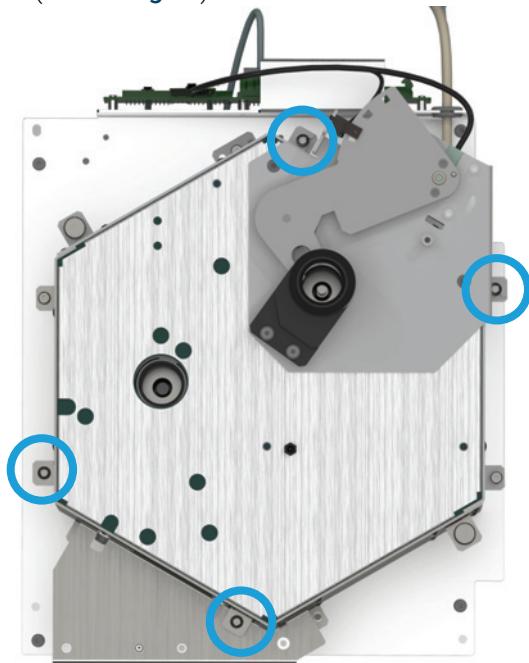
Entfernen Sie die T-20-Torx Schrauben von der oberen Ofenbaugruppe.
